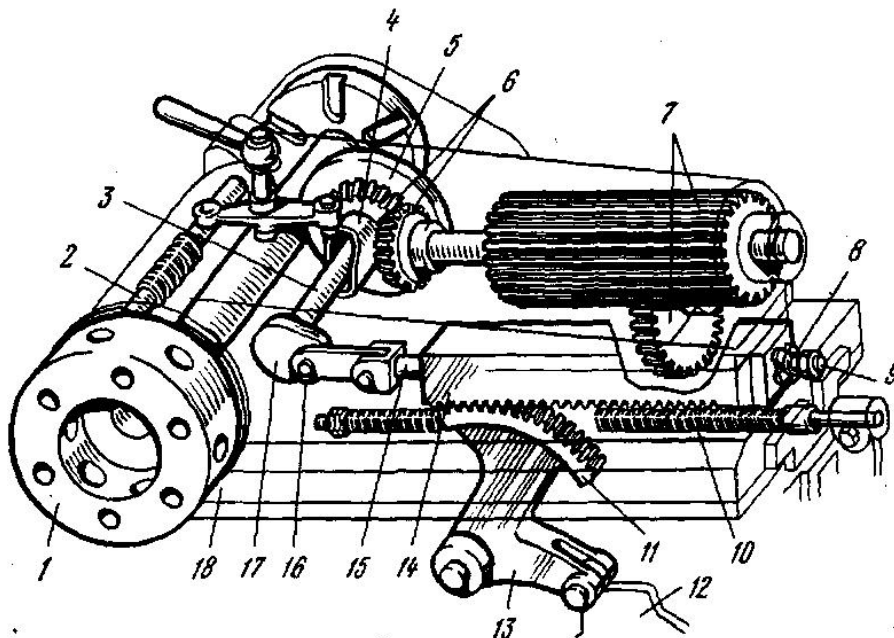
Поздовжній супорт з револьверною головкою токарно-револьверних автоматів
